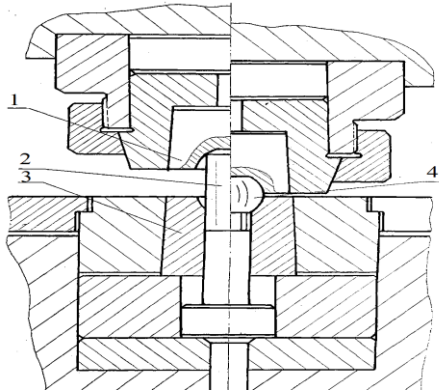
Конструктивна схема штампа, призначеного для висадження сферичних заготовок: 1 – пуансон, 2 – заготовка до висадження, 3 – матриця, 4 – заготовка після висадження.
